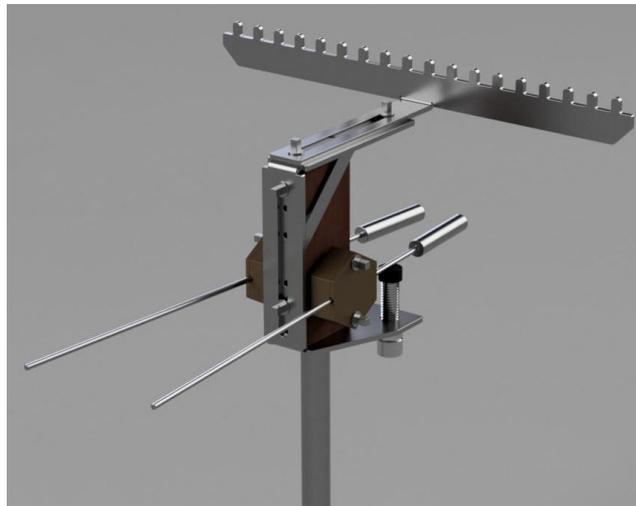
Imagem explodida do *sketch* final do SIBAPIS2020.
